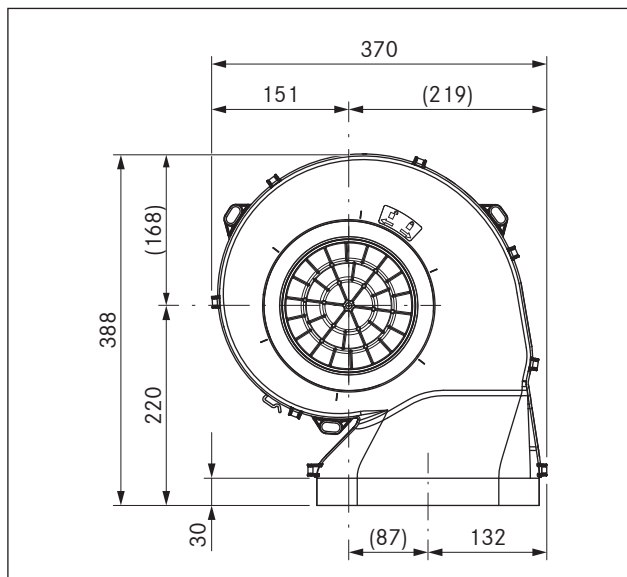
Dimensioni apparecchio ULS vista da sopra
